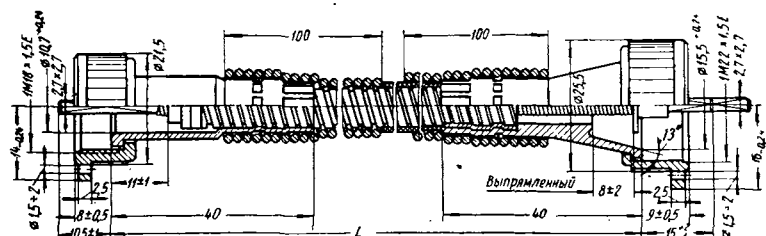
Привод ГВ10-Б (зап. ч.), поверх брони ставится резиновая трубка толщиной 1—2 мм; гайки и присоединительные размеры ниппелей одинаковы с обеих концов.
